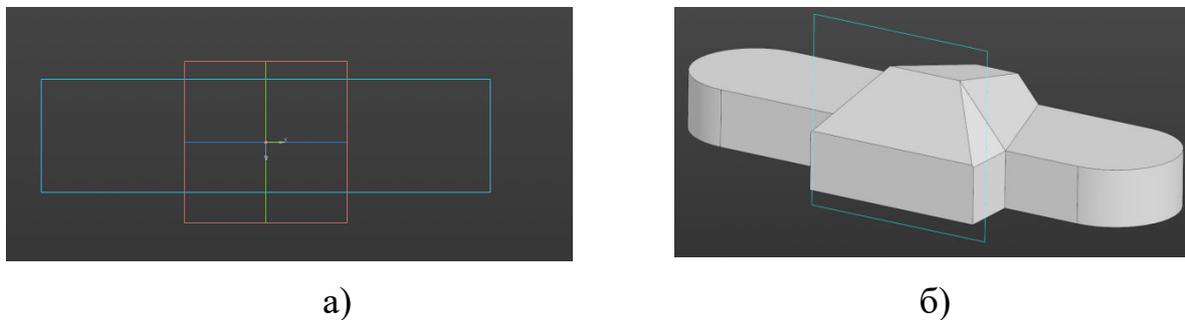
Создание модели верхней части корпуса: а) эскиз корпуса; б) крышка корпуса
